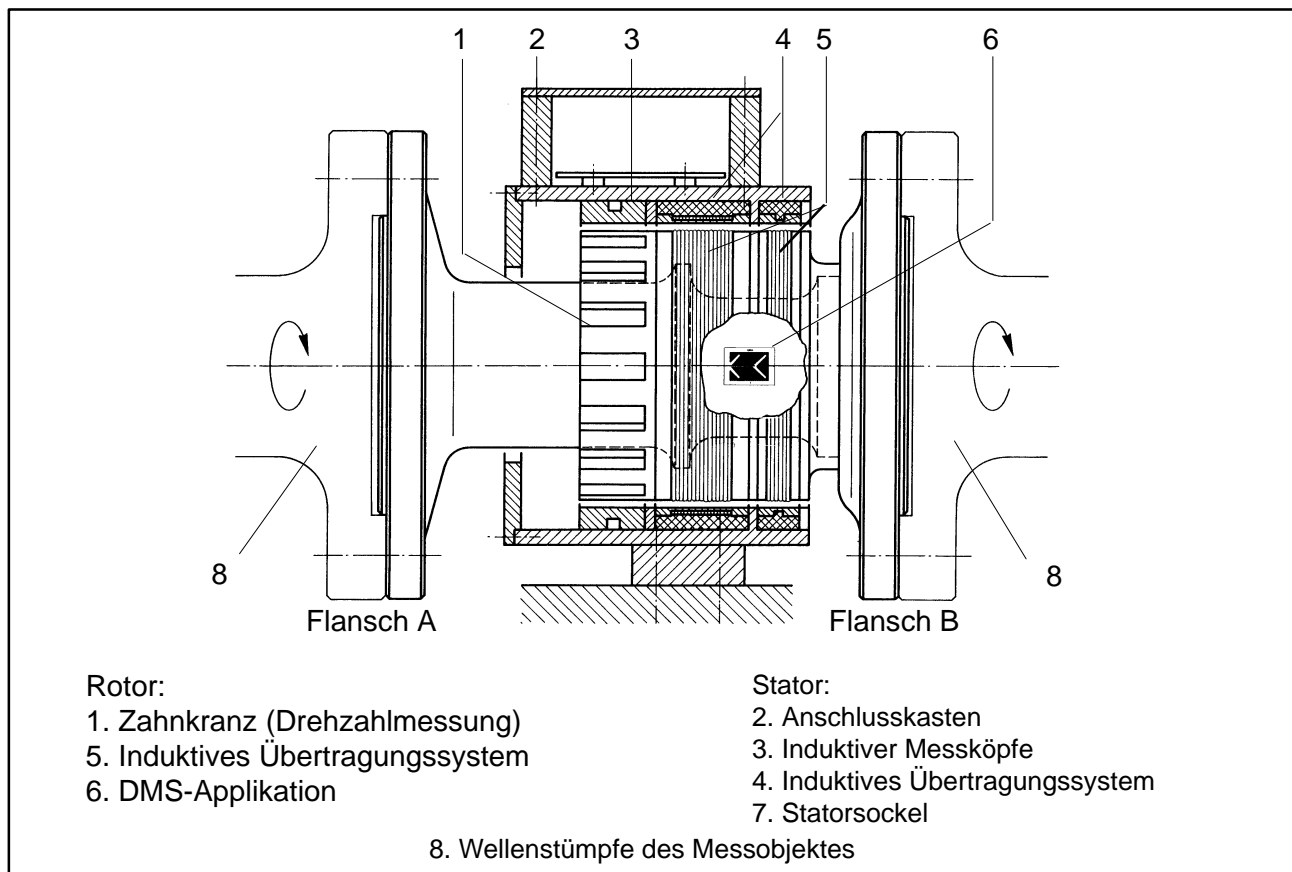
Mechanischer Aufbau, Prinzipzeichnung
